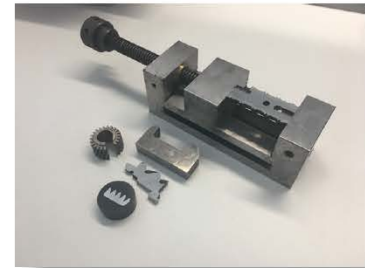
Универсальные держатели для нескольких образцов (слева)
